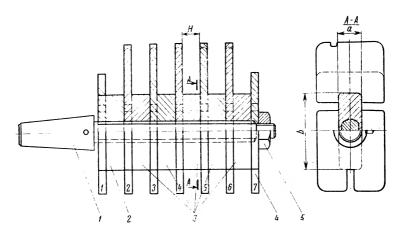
Приспособление для намотки нескольких катушек статора одним проводом
